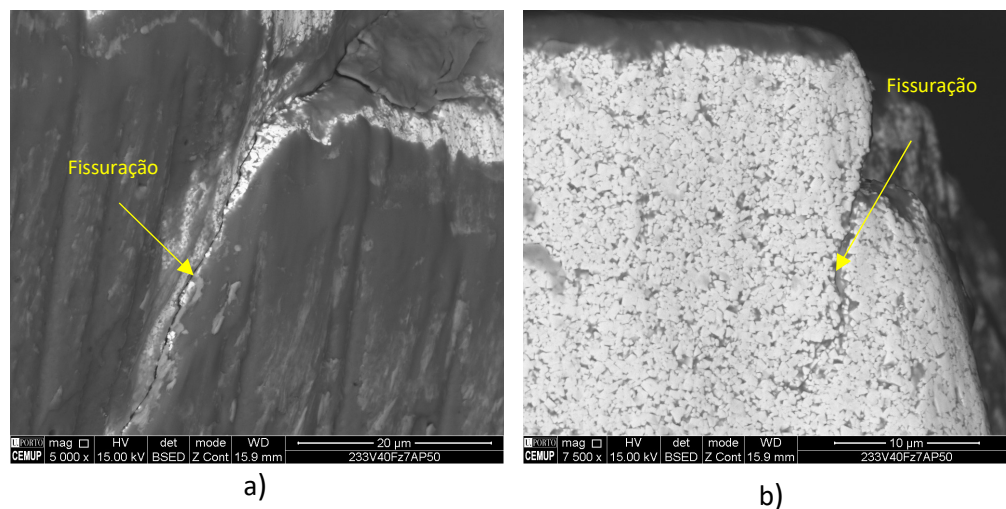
Fissuração presente no ensaio V1F2A1 da ferramenta 233: a) aresta da ferramenta e b) parte inferior da ferramenta.
